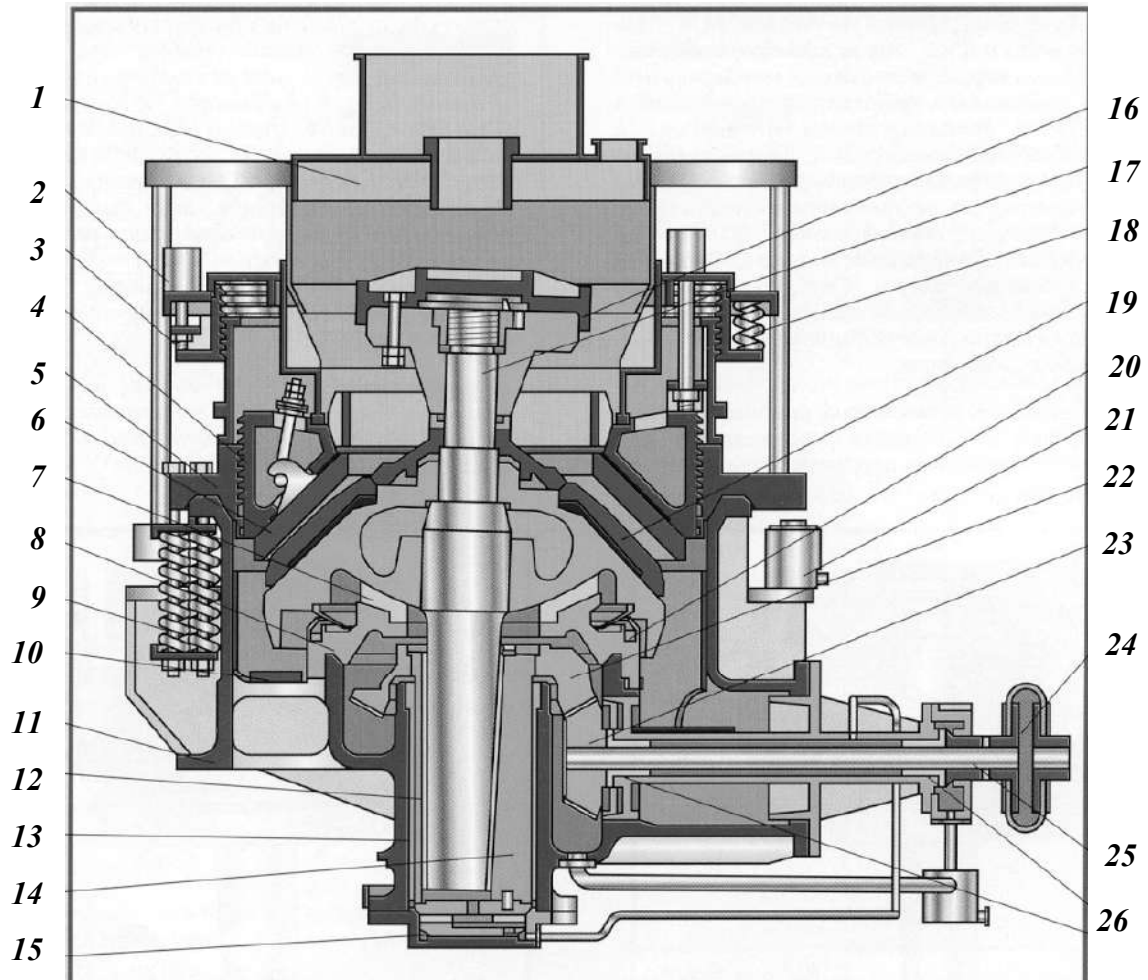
Конусна дробарка типу КМД-2200Т.
